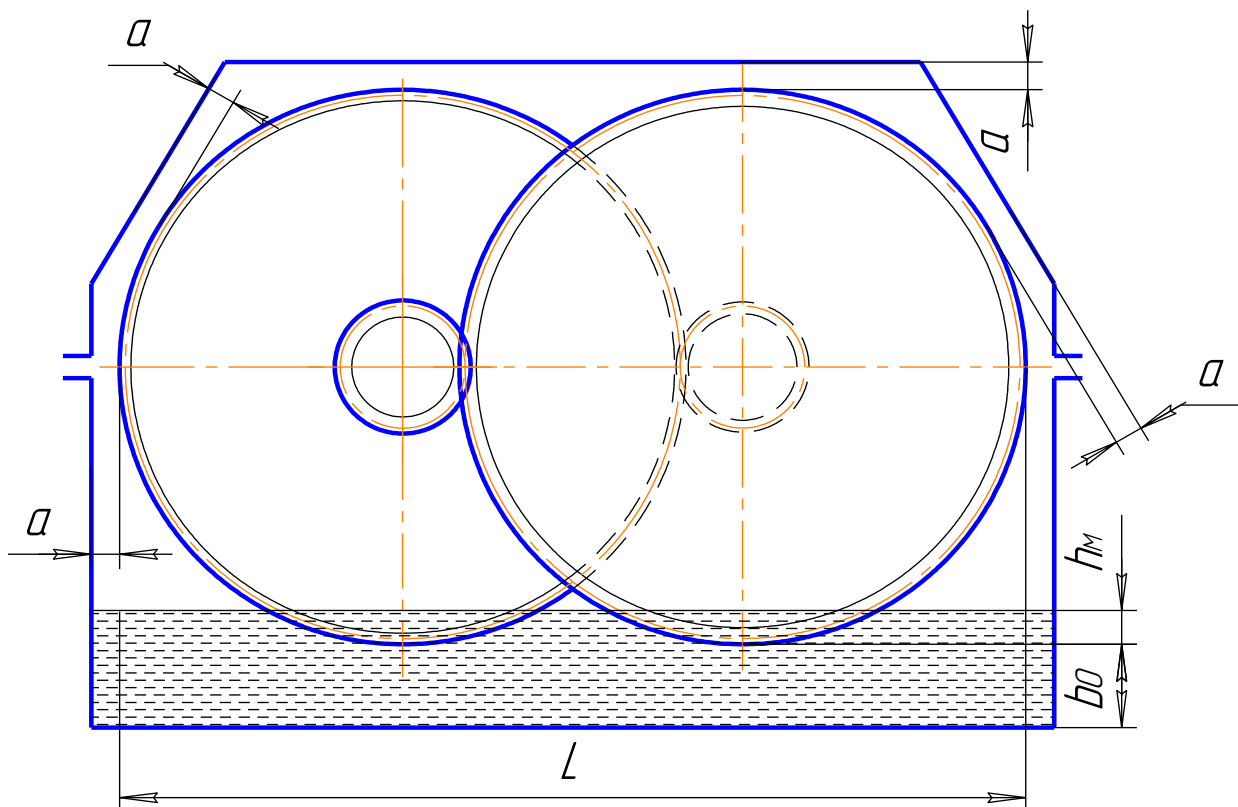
Компонка цилиндрического двухступенчатого соосного редуктора.
